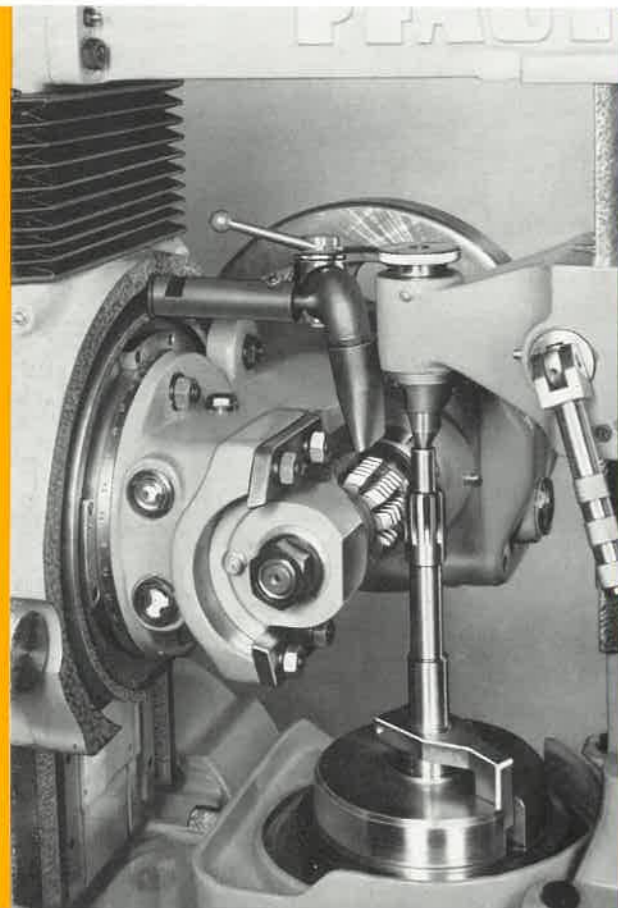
Fräsen einer Keilwelle im Gegenlauf-Verfahren
